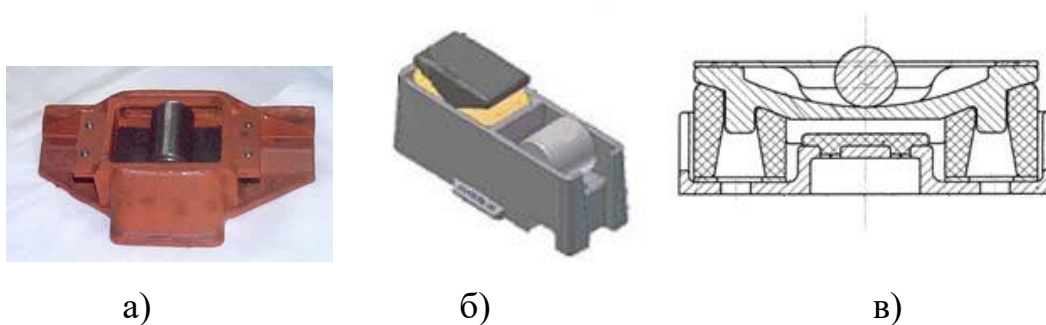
Конструкции катковых и упруго-катковых боковых скользунов:
